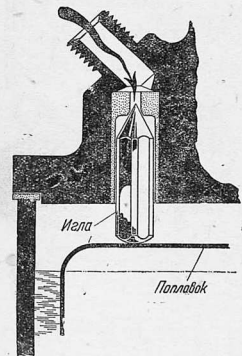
Игольчатый клапан поплавковой камеры карбюратора
